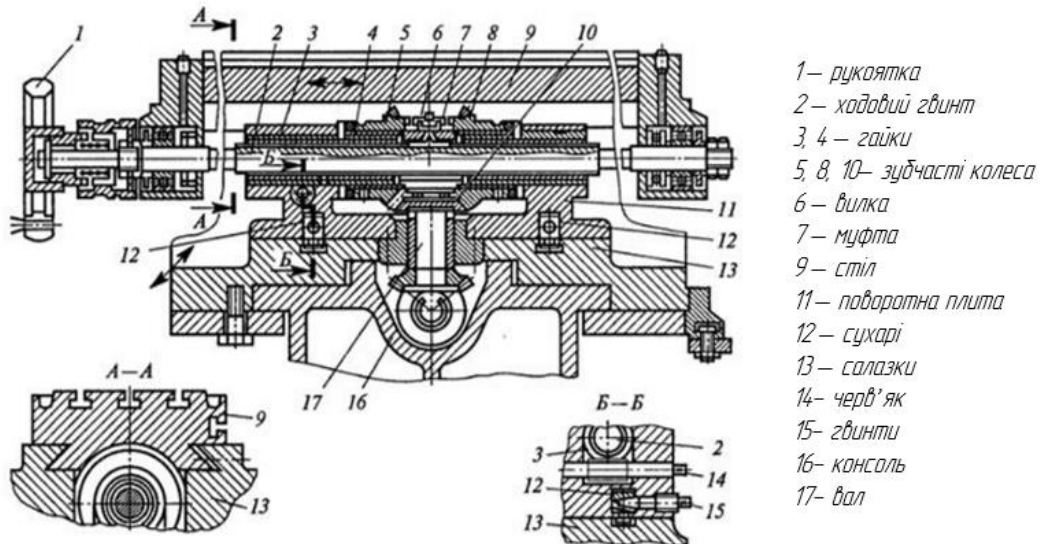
Розріз столу і салазок верстату повздовж ходового гвинта
